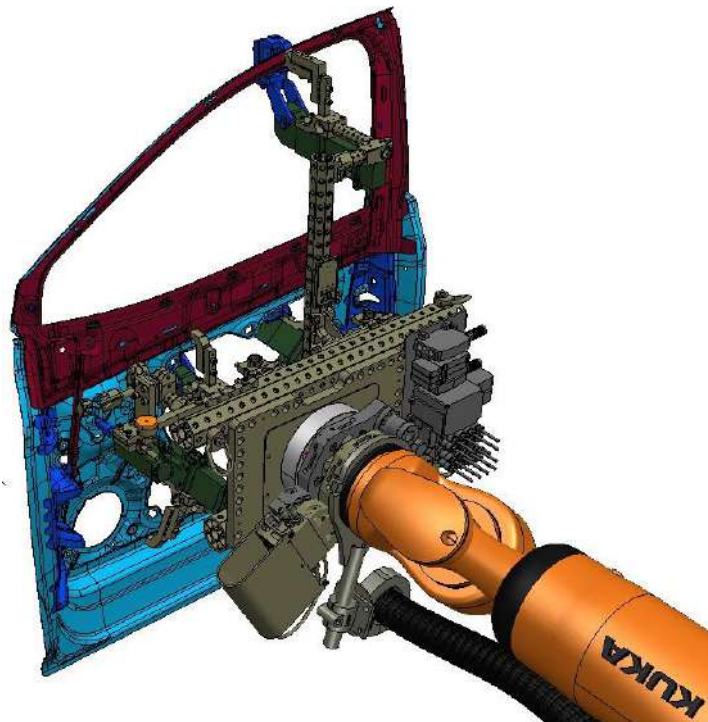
Калібрування стаціонарного зварювального пістолета пристрою
